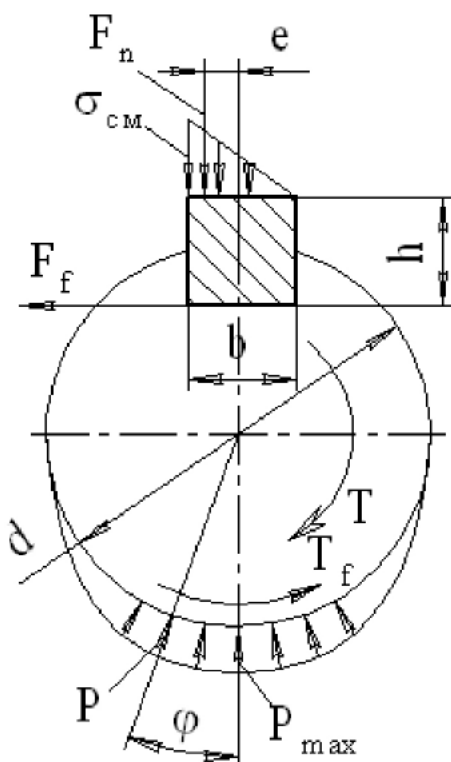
Схема нагружения соединения с клиновой шпонкой
